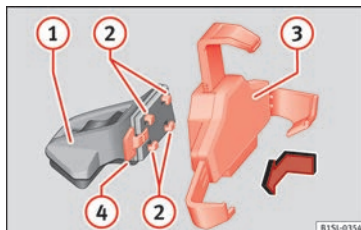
Assemblare il supporto universale e il braccio di sostegno.
